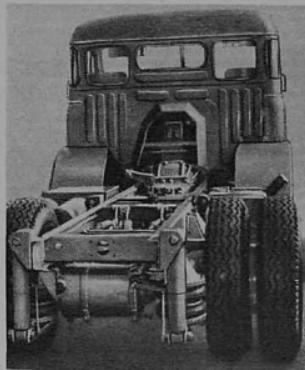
Установка пневматической подвески на шасси грузового автомобиля.
